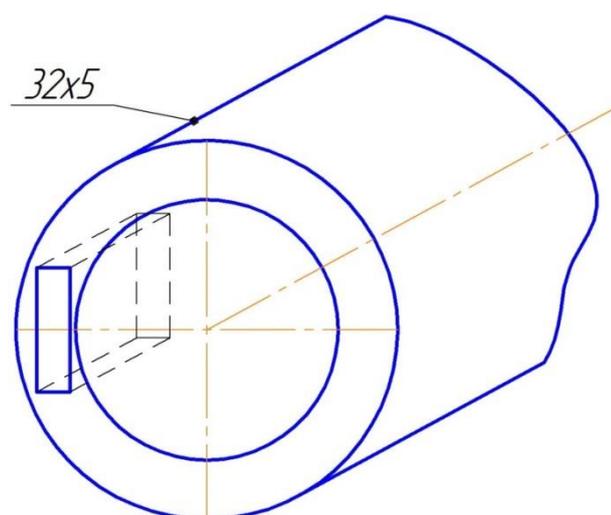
Образец трубной стали 12Х1МФ
